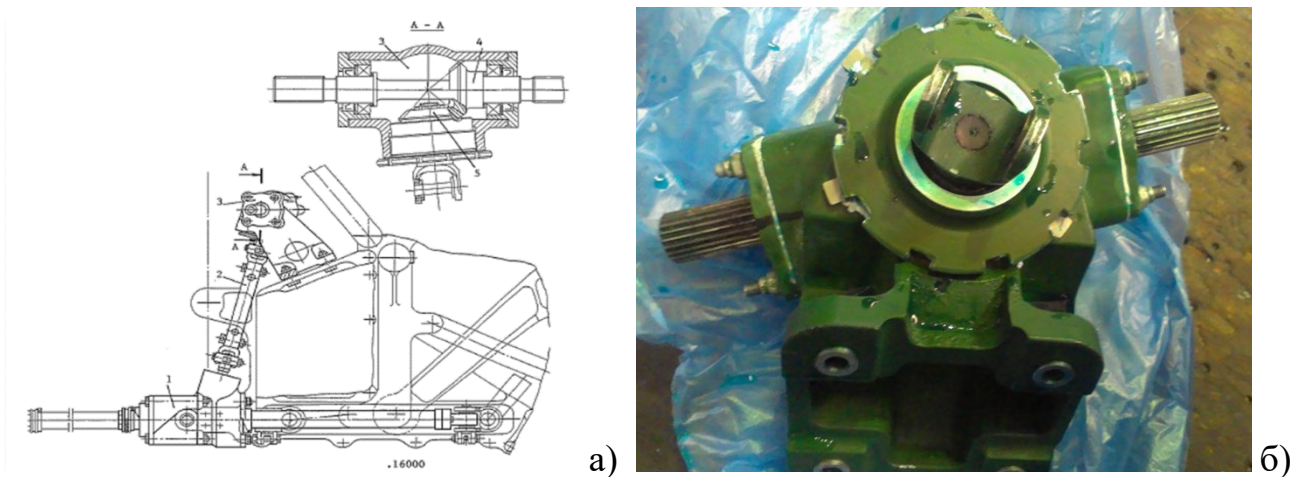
Установка підйомника № 1 на нервюрі крила №6: а) – конструктивна схема та розташування конічного редуктора, б) – фото конічного редуктора.
